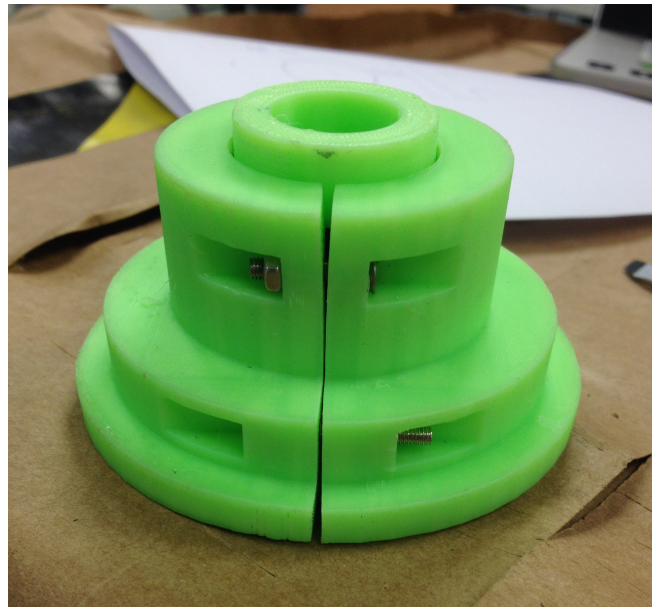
Laminado. Ensamble del molde con la laminación realizada. (Fuente: Propia)
